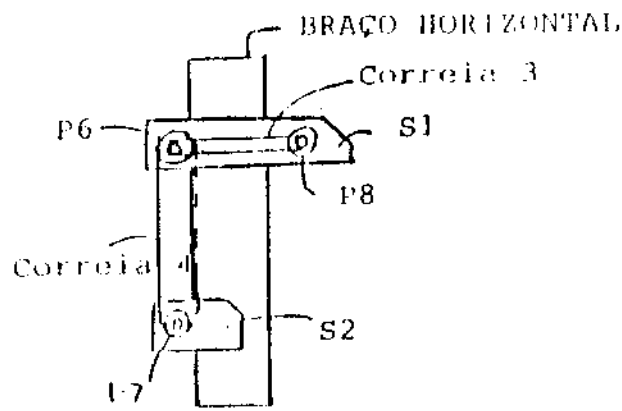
b- Vista inferior do braço horizontal (detalhe de transmissão do movimento).
